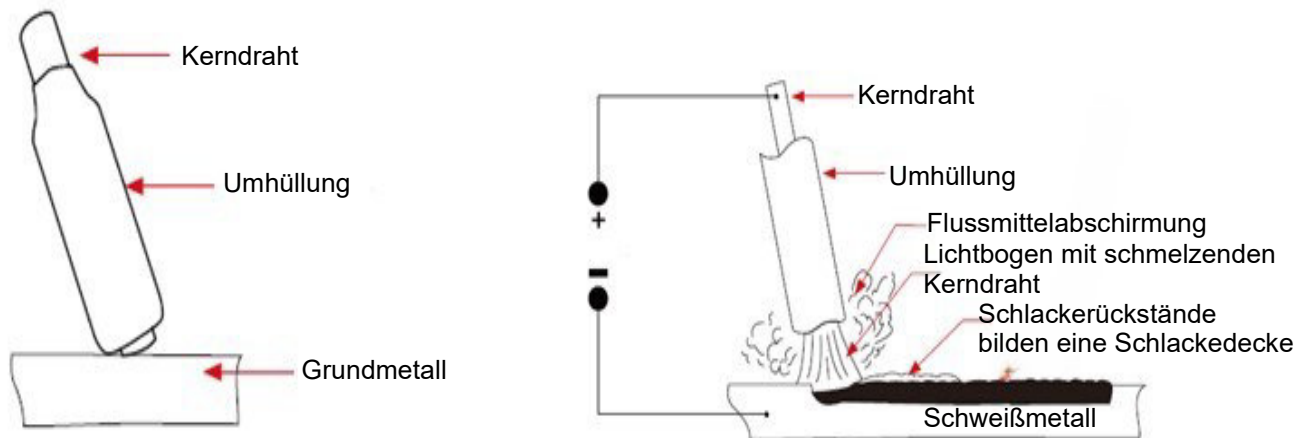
MMA/Stick Elektrodenschweißen
